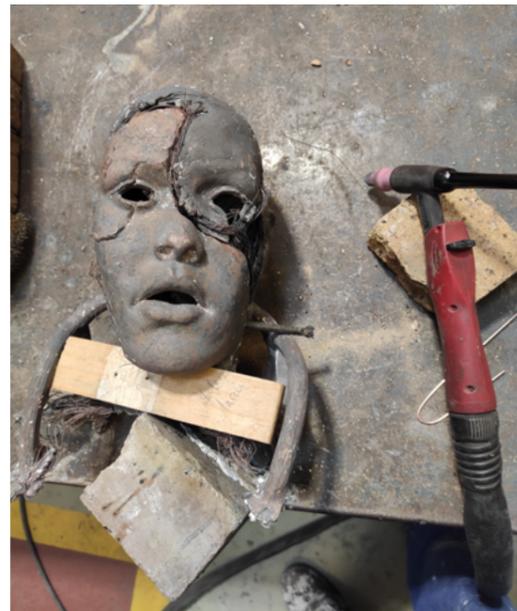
Diego Vidal. Soldado de la cara al resto de la cabeza.
